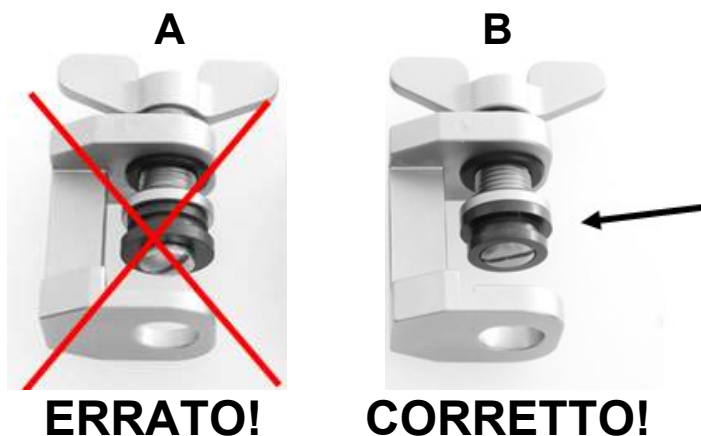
Rappresentazione del montaggio errato (A) e corretto (B) dell'elemento di fissaggio
